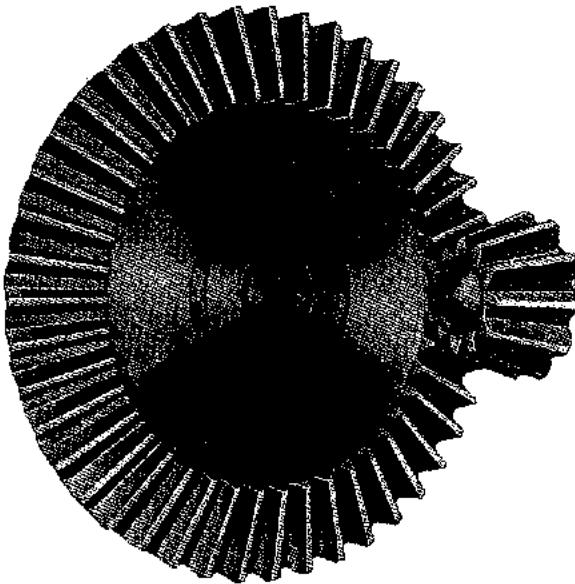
Engranaje de rueda y piñón cónicos (Philadelphia Gear Works)
